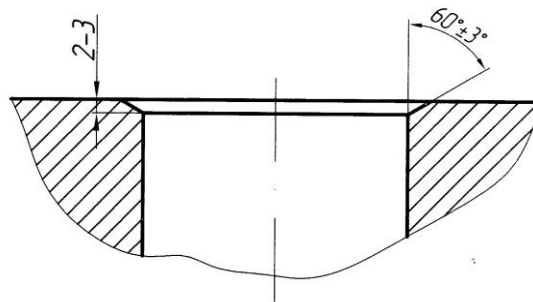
Подготовка кромок отверстий в верхней трубной решетке под приварку трубок
